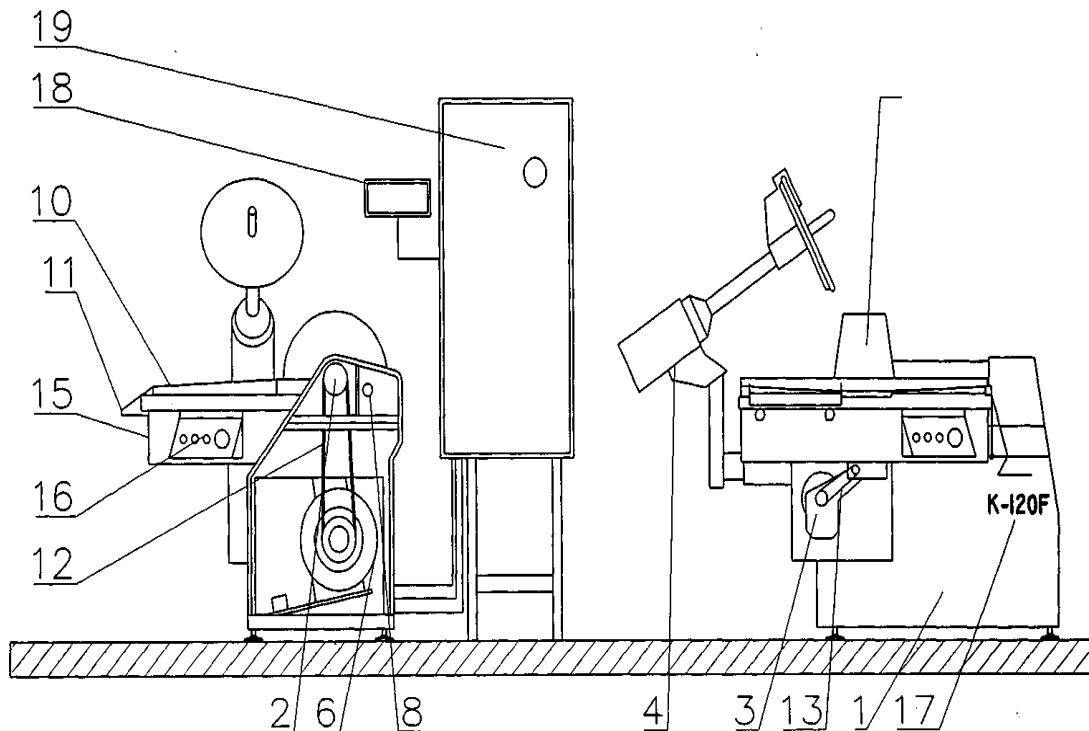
Загальний вигляд: 1 – корпус; 2 – ножовий вал; 3 – привід чаш; 4 - вивантажувач; 6 - електродвигун валу ножів; 8 – магніт; 9 – кожух головки; 10 – кожух чаш; 11 – жолоб вивантажування; 12 – паси ножового валу; 13 – привід чаші; 15 – кожух бічний чаші; 16 – пульт; 17 – щиток; 18 – дисплей; 19 – шафа.
